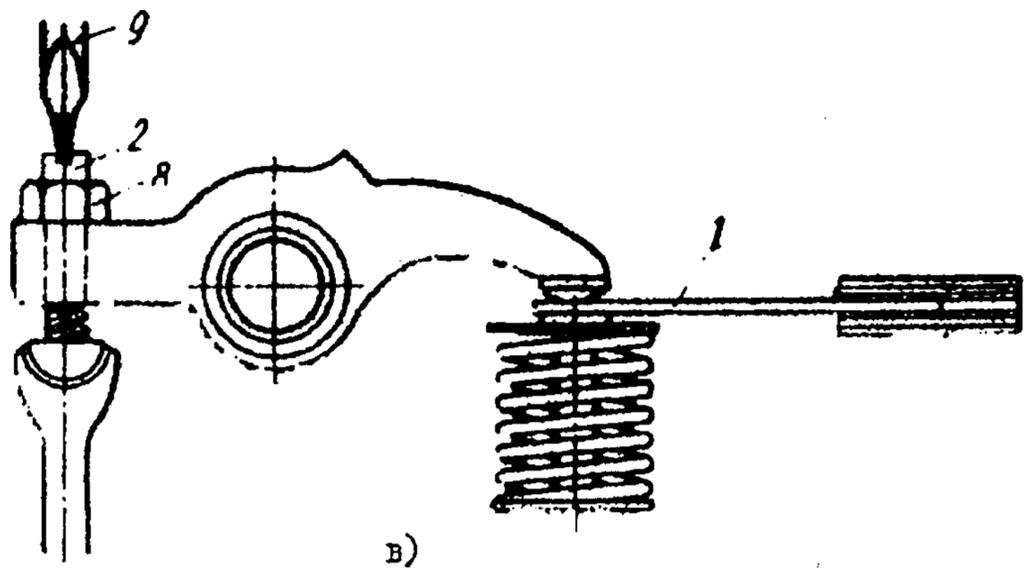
Схема проверки щупом и регулировки теплового зазора в механизмах газораспределения:
